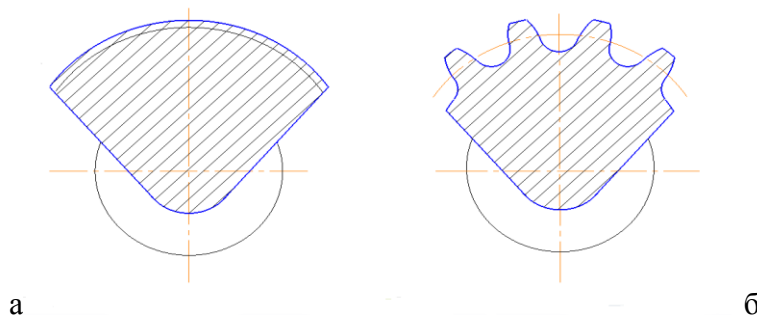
Общий вид поковки зубчатого венца вала сектора 453461.400/002, сталь 25ХГТ. а – первоначальный, б – предлагаемый.
